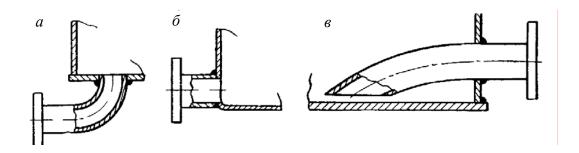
Приварка сливных патрубков: a — приварка патрубка к днищу аппарата;  $\delta$  — приварка патрубка вровень с днищем;  $\epsilon$  — изогнутый патрубок
